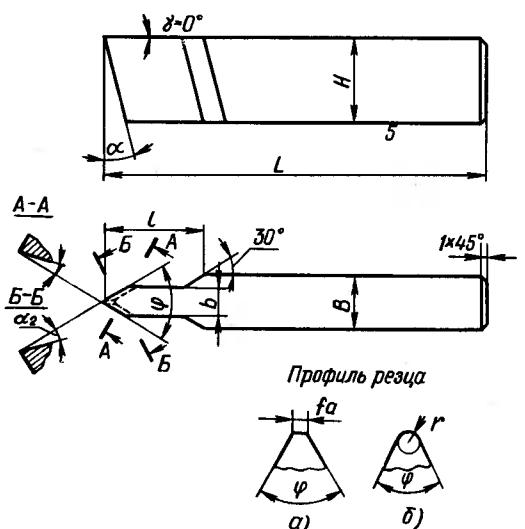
Стержневой резьбовой резец из быстрорежущей стали
